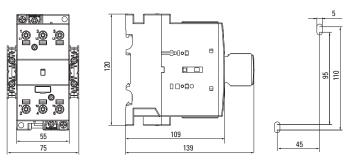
Габаритные и установочные размеры контакторов КМЭ 50А, КМЭ 60А, КМЭ 65А
